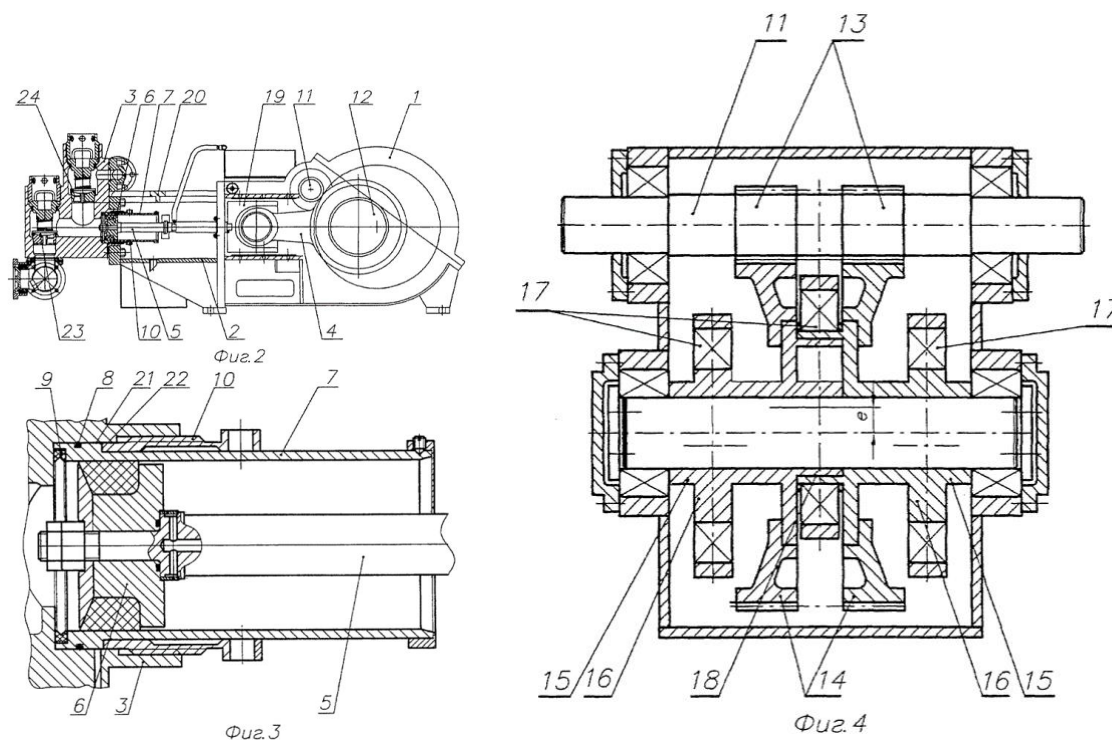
Ескіз до патенту 2328621 «Поршневий насос»: 1-привід; 2-блок циліндрів; 3-клапанна коробка; 4-шатун; 5-шток; 6-поршень; 7-гідроциліндр; 8,9-ущільнення; 10-встановлююча гайка; 11-трансмійний вал; 12-головний вал; 13-пара ведучих коліс; 14-зубчаті вінці; 15-ступиця; 16-ексцентрик; 17-підшипник; 18-посадка; 19-крейцкопф; 20-несучий траверс; 21-циліндричний пояс; 22-торцева поверхня; 23,24-клапани.
